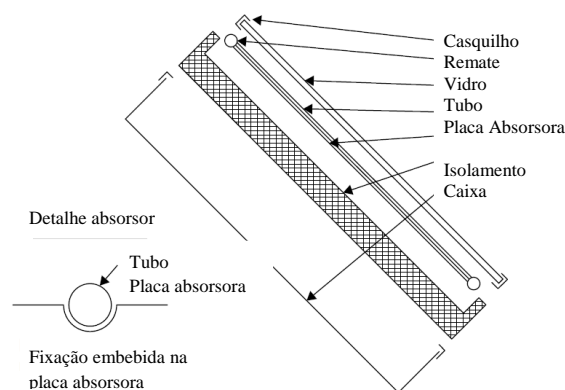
Esquema de construção de coletor plano, (Kalogirou 2009)
